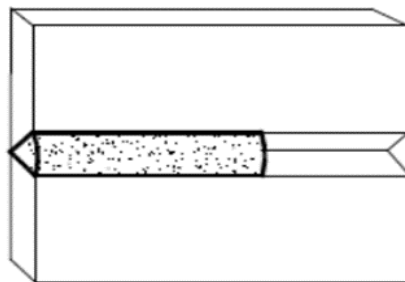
Soldadura horizontal. Rodríguez (2016).
